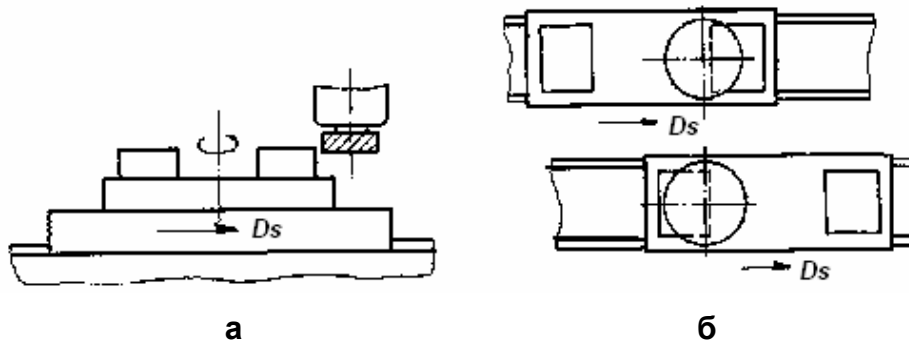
Оброблення на двопозиційному верстаті (а) і "маятникове" оброблення (б)
